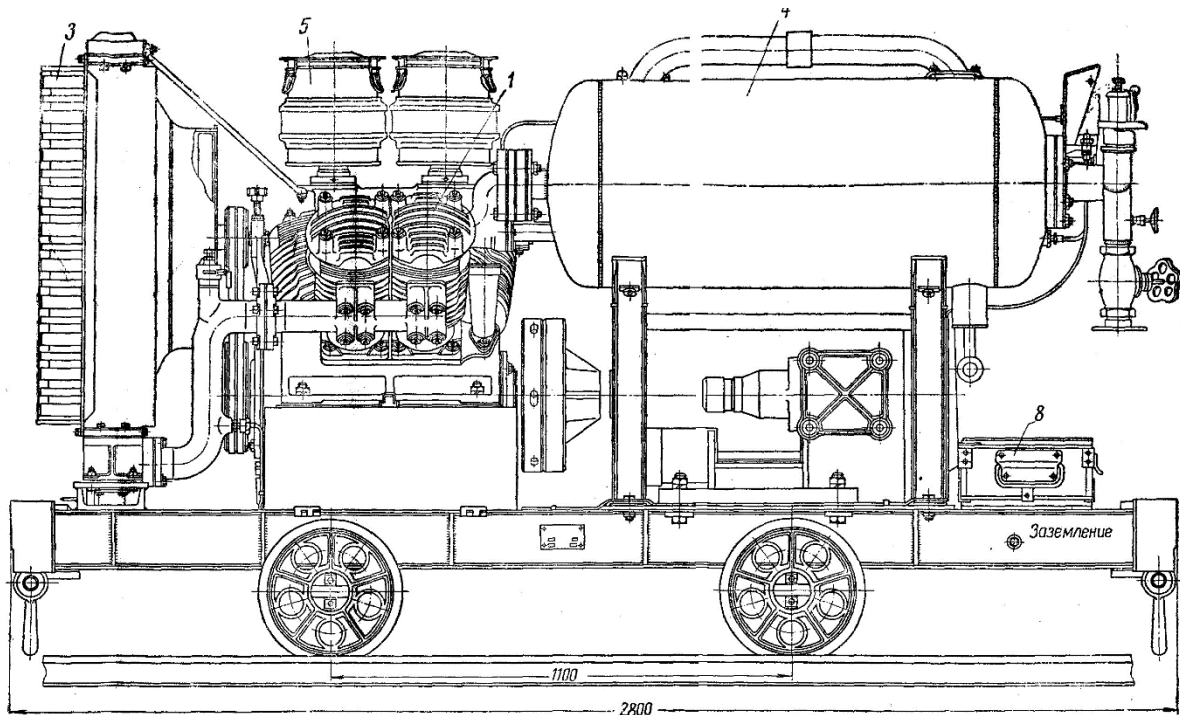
Общий вид станции ЗИФ – ШВКС – 5
